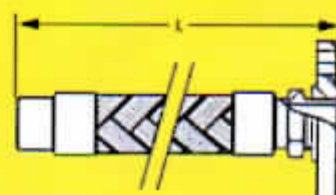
ponta soldada e macho fixo com flange roscado
